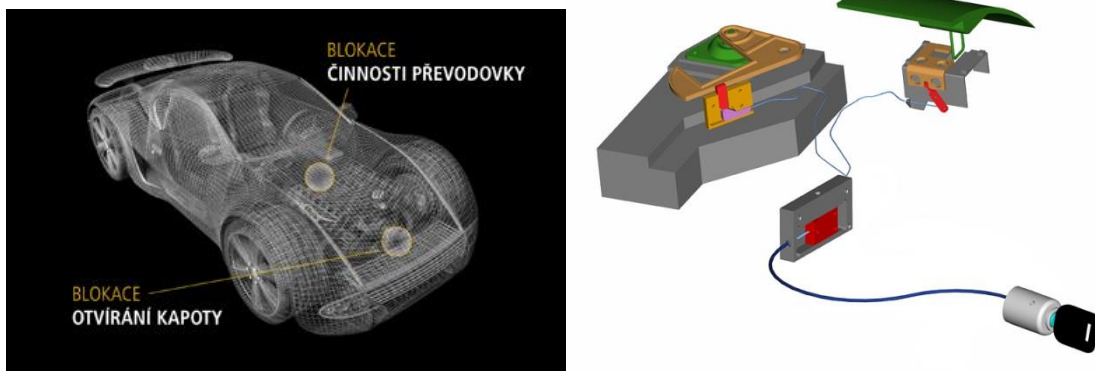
Zámek řadicí páky DEFEND LOCK a CONSTRUCT [13]
